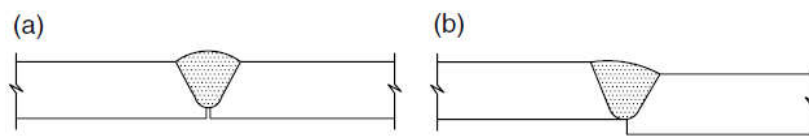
Défauts de soudure : a) le manque de pénétration et b) le manque d'alignement
